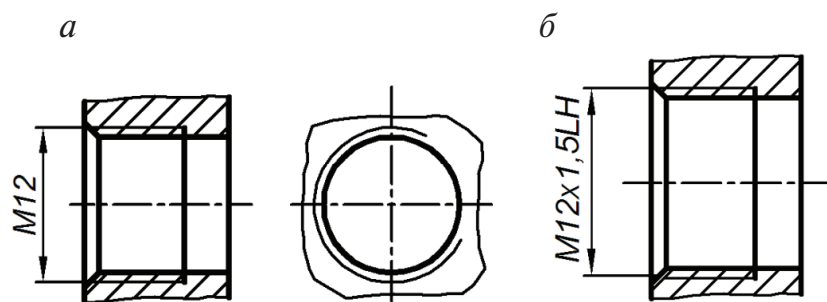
Пример изображения на чертеже внутренней метрической резьбы (в отверстии):
